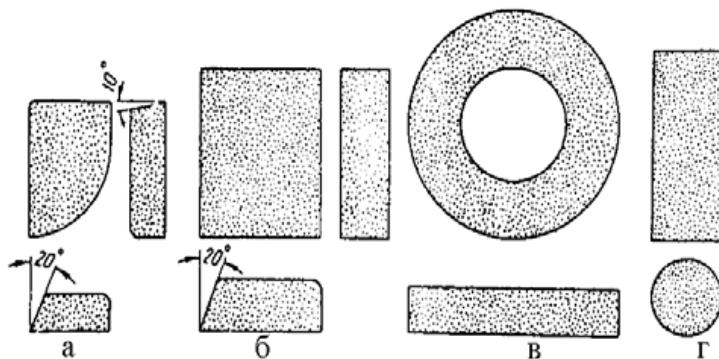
Форми твердосплавних пластин, що використовуються для оснащення різальної частини торцевих фрез (а – пластина фасонна; б – пластина прямоугольна; в – твердосплавний диск; г – твердосплавний циліндр-стовпчик)
